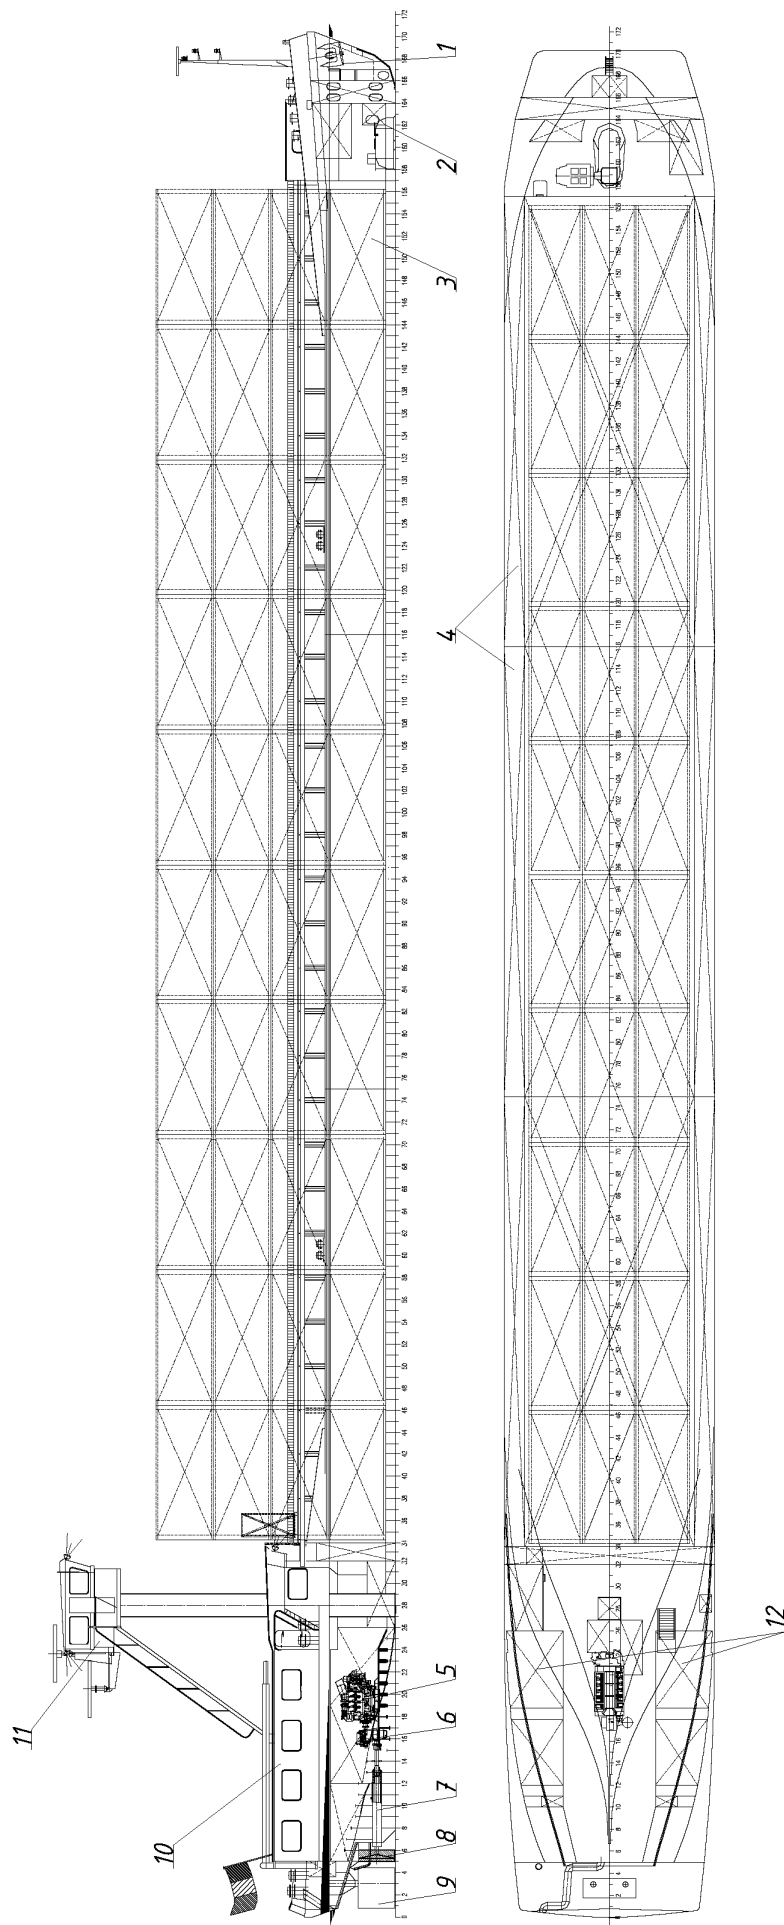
Креслення загального вигляду судна «ARAGON». 1 – якірний клюз; 2 – підрулюючи пристрій; 3 – вантажний трюм; 4 – баластні цистерни; 5 – головний двигун; 6 – головний редуктор; 7 – валова лінія; 8 – гвинт; 9 – перо руля; 10 – надбудова; 11 – штурманська рубка; 12 – цистерні основного запасу
